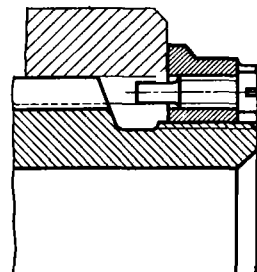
Стопорение кольцевой гайки с торцовыми зубьями винтом
